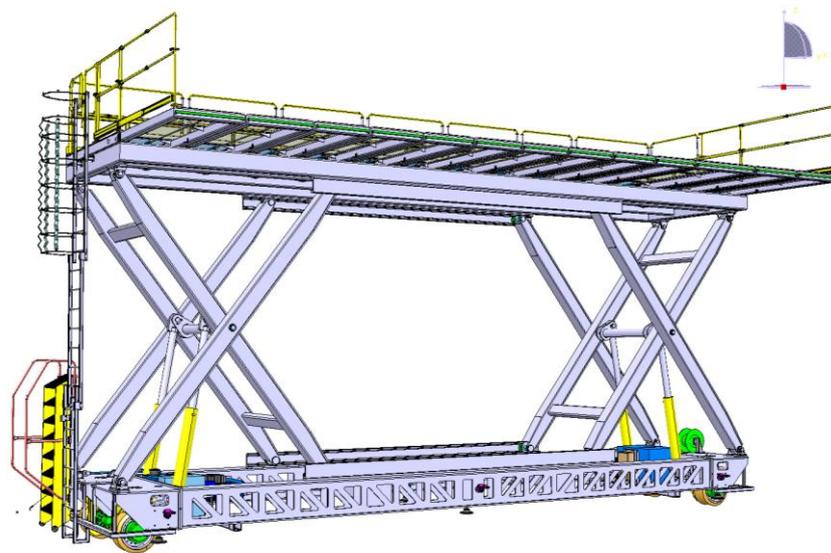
Detalle del montaje de la tijera en la plataforma elevadora
